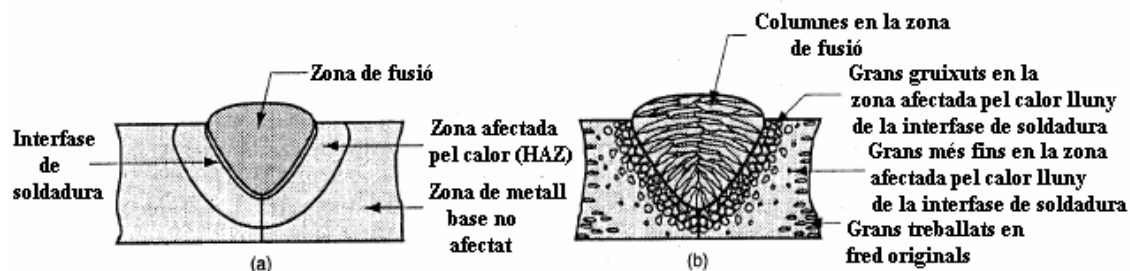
Secció transversal d'una junta soldada per fusió comú.
